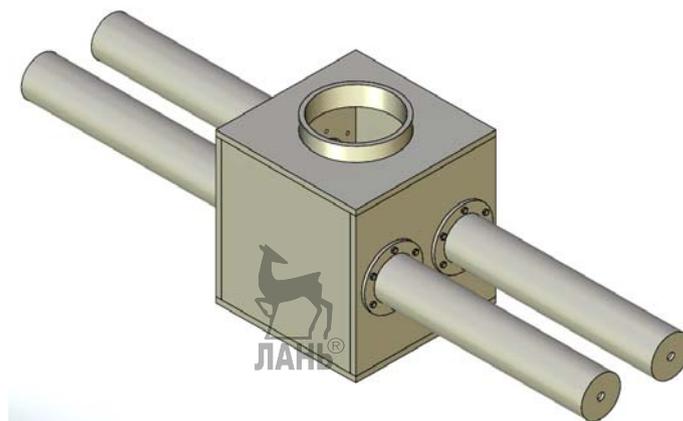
Сборка «Корпус опорно-поворотного устройства»
